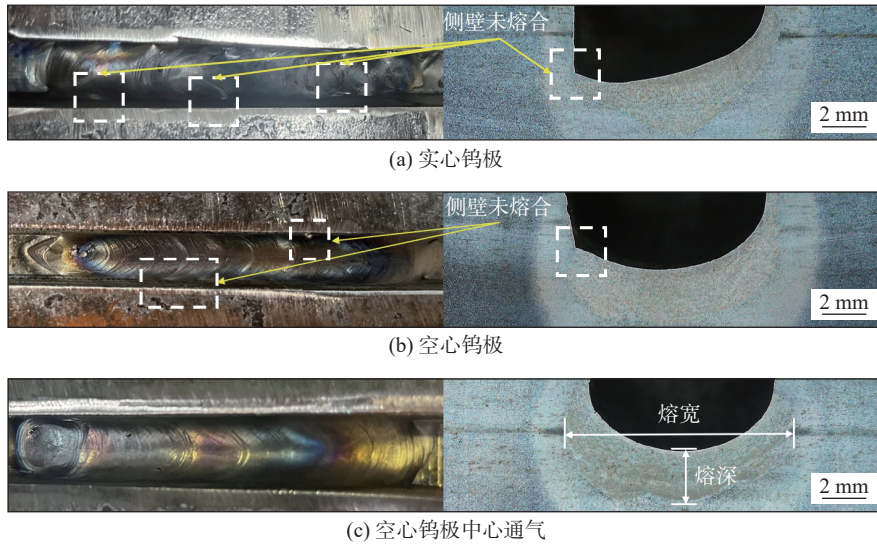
不同钨极结构下的焊缝表面成形及焊缝截面形貌
